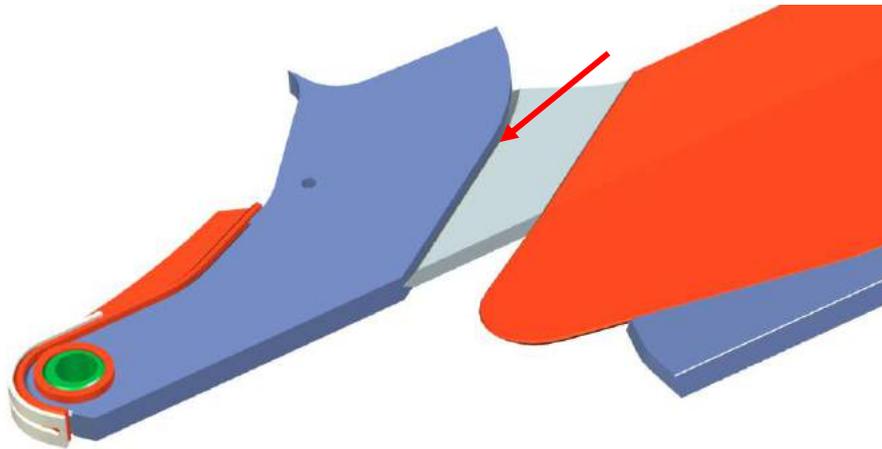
Ejemplo de buena práctica de alternar soldaduras en doble bisel (Lado B)
